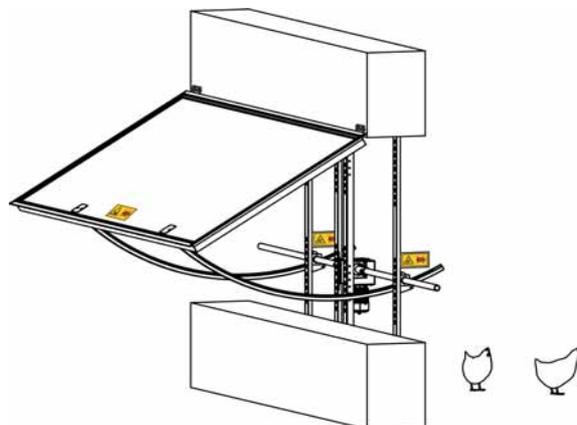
Туннельная заслонка с шарнирным креплением сверху - открытие наружу помещения
